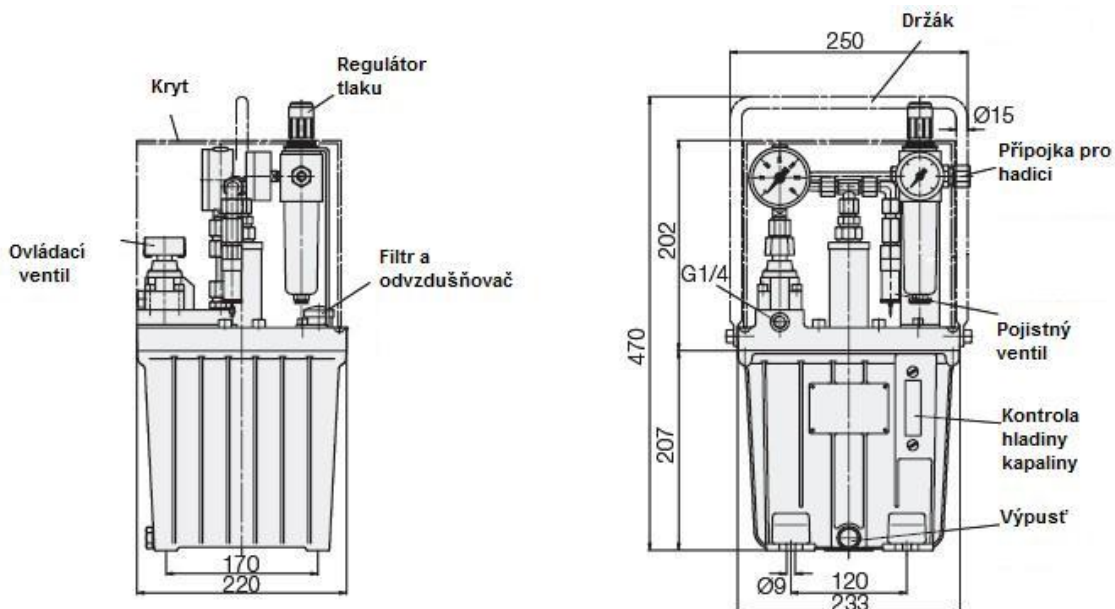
Parametry pneumatického pístu Roemheld 1. 450[12]
